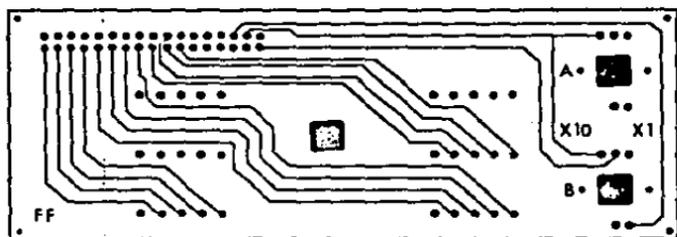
Circuito impreso "de interruptores" lado de soldadura.
